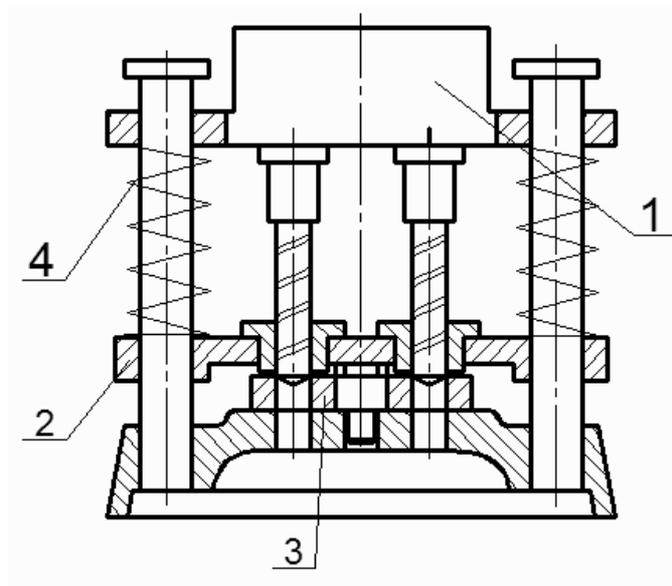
Схема зажимного устройства сверлильного станка.
